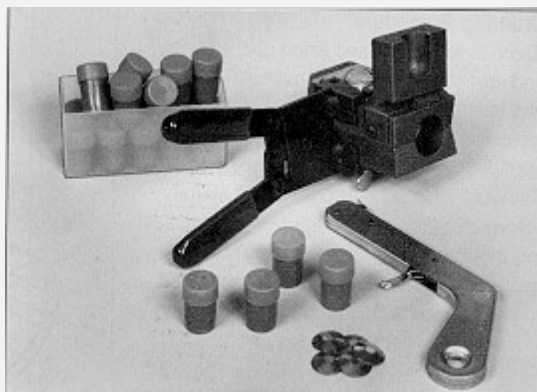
Kit para soldaduras aluminotérmicas
